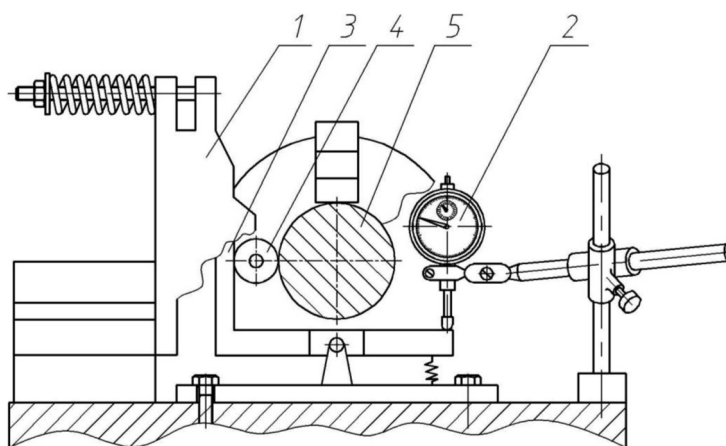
Схема эксперимента. 1 – обкатник; 2 – индикатор; 3 – рычажное устройство; 4 – деформирующий ролик; 5 – обрабатываемая заготовка
